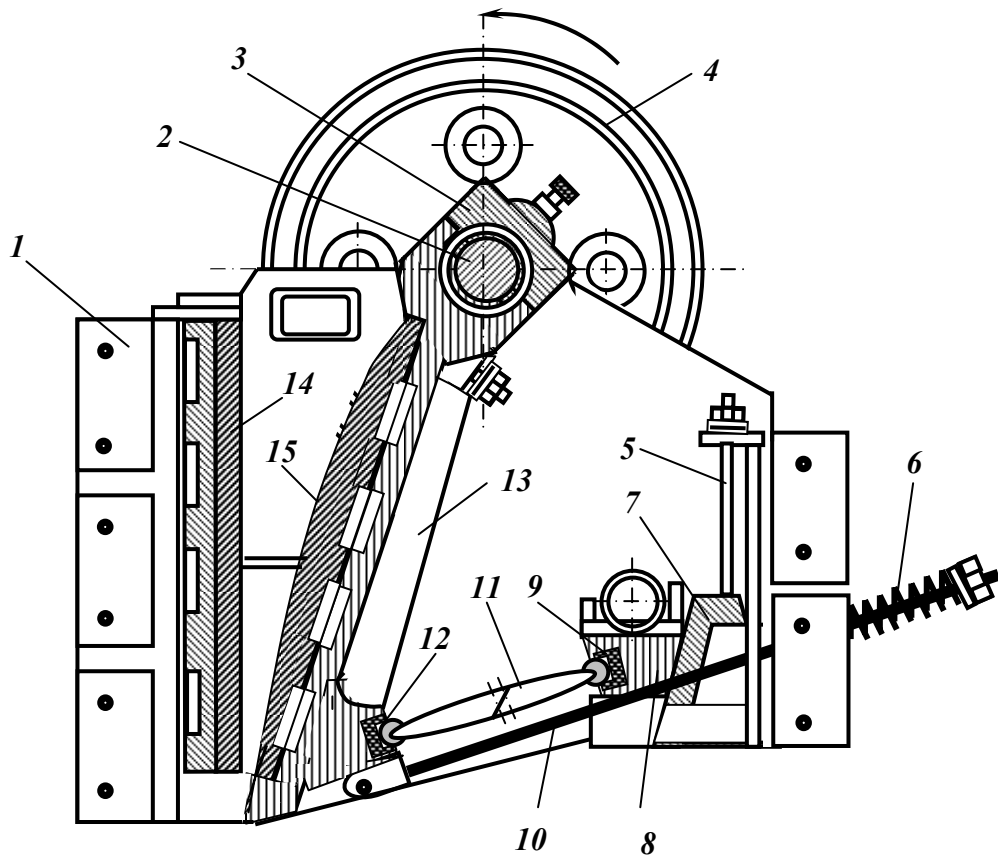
Щокова дробарка зі складним рухом щоки типу ЩДС.
